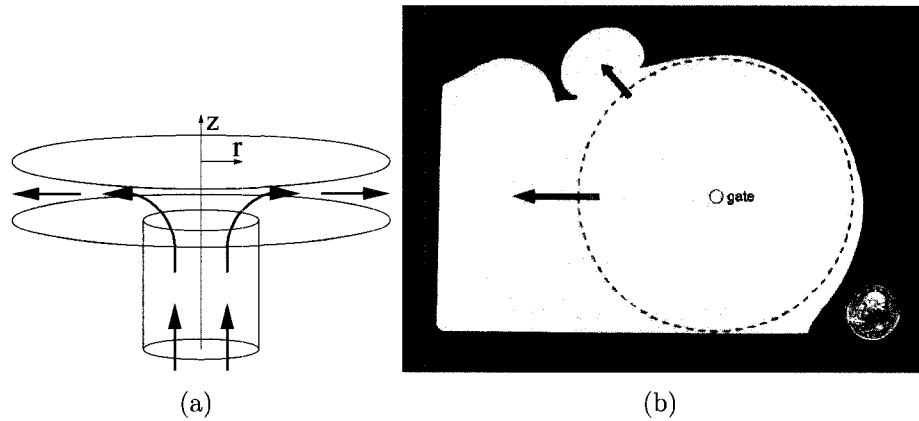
Schéma de l'injecteur (a) et défauts de fabrication engendrés par des instabilités de l'écoulement (b).
